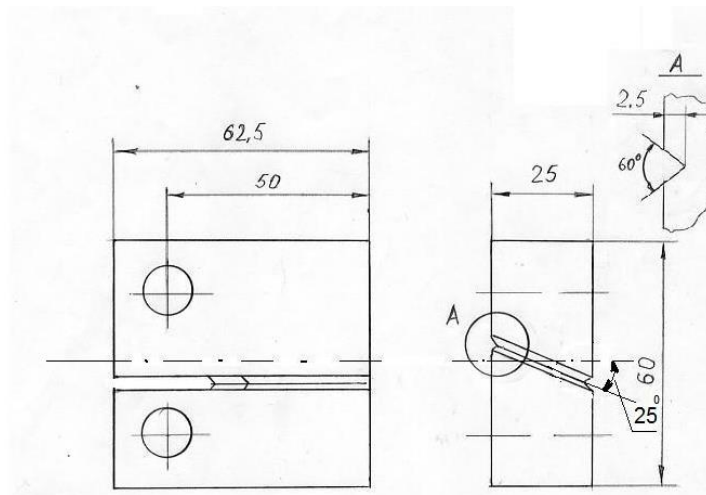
Модифицированный компактный образец с косой трещиной [6].
